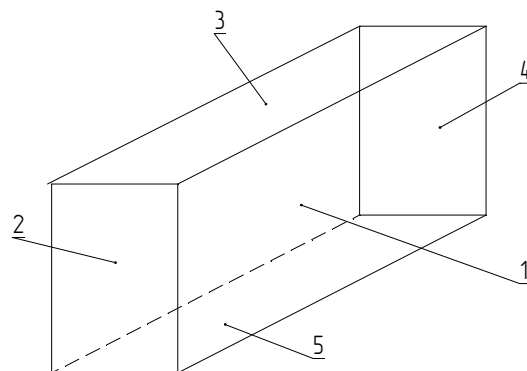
Схема видов механической обработки граней образцов (1 – чистовое фрезерование; 2 – рубка на ножницах гильотинного типа; 3 – грубое фрезерование; 4 – шабрение; 5 – чистовое шлифование)
